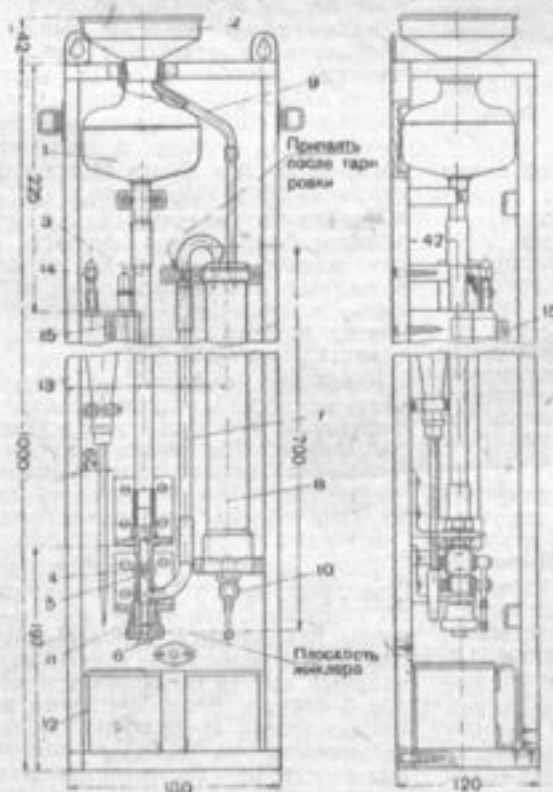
Сборочный чертеж прибора конструкции инж. П. Тарасова для проверки жиклеров
